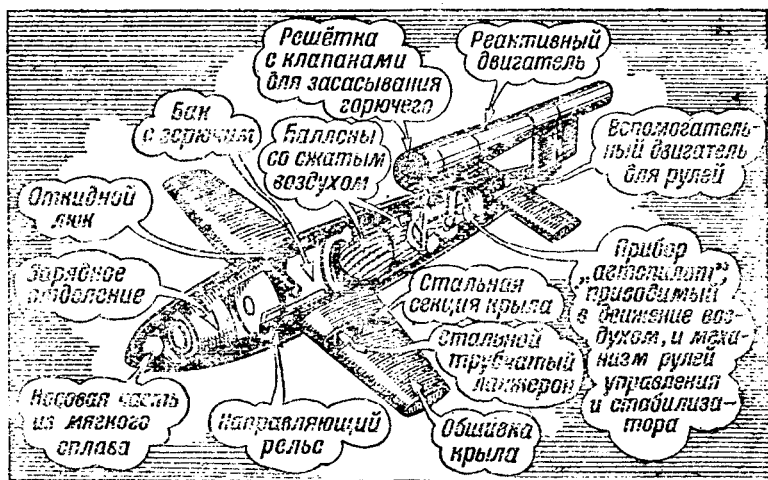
Схематический чертёж устройства немецкого «самолёта-снаряда».
